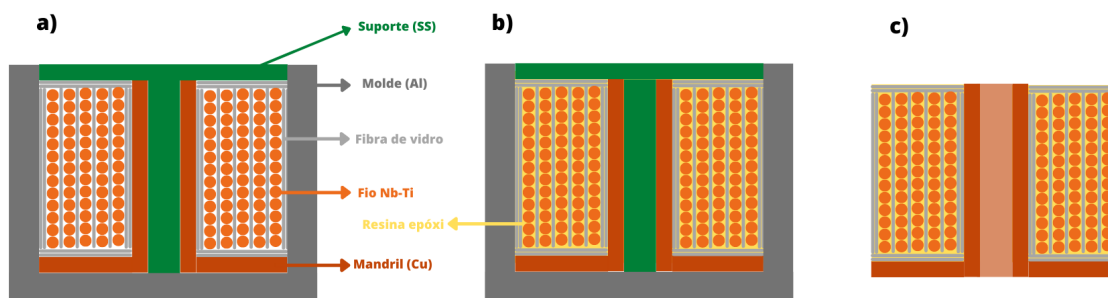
Representação das bobinas impregnadas à vácuo: a) conjunto da bobinagem inserido no molde de impregnação; b) resina epóxi impregna o conjunto; c) bobina impregnada. Fonte: adaptado de [19]
